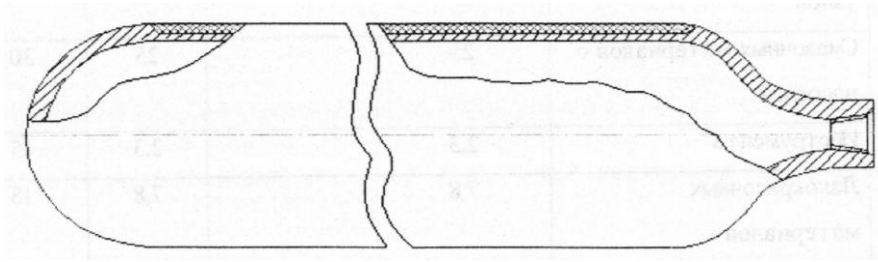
Баллон металлопластиковый с армирующей оболочкой по цилиндрической части.
